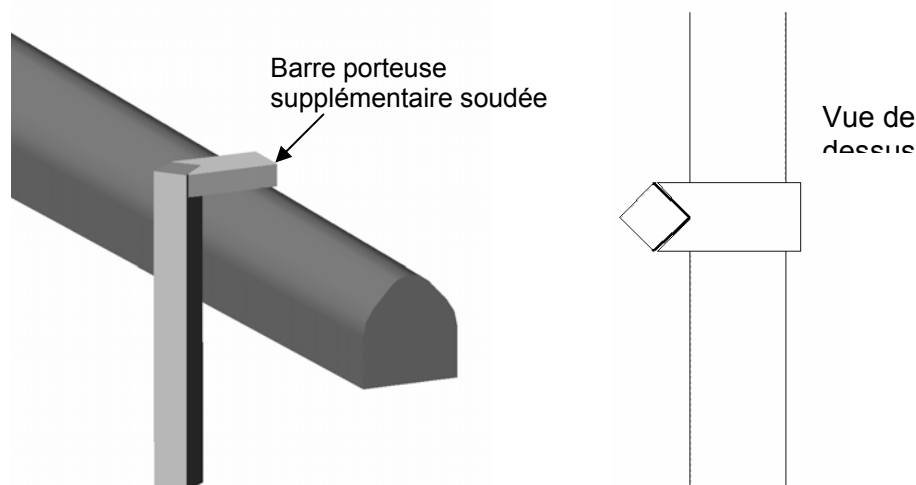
Barre carrée de montage soudé au bras de la pale racleuse
